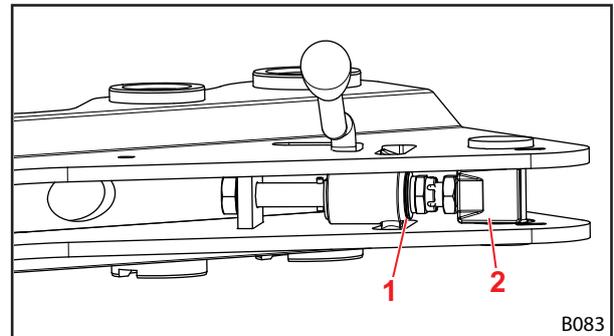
Vista del dispositivo di bloccaggio del caricatore frontale dal basso
